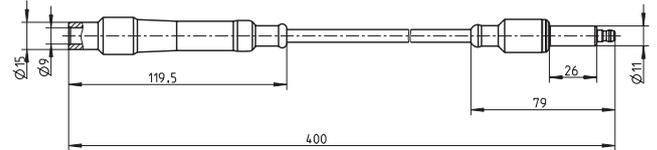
Zündkabelverlängerung Typ 1500A97 (L = 400 mm)
